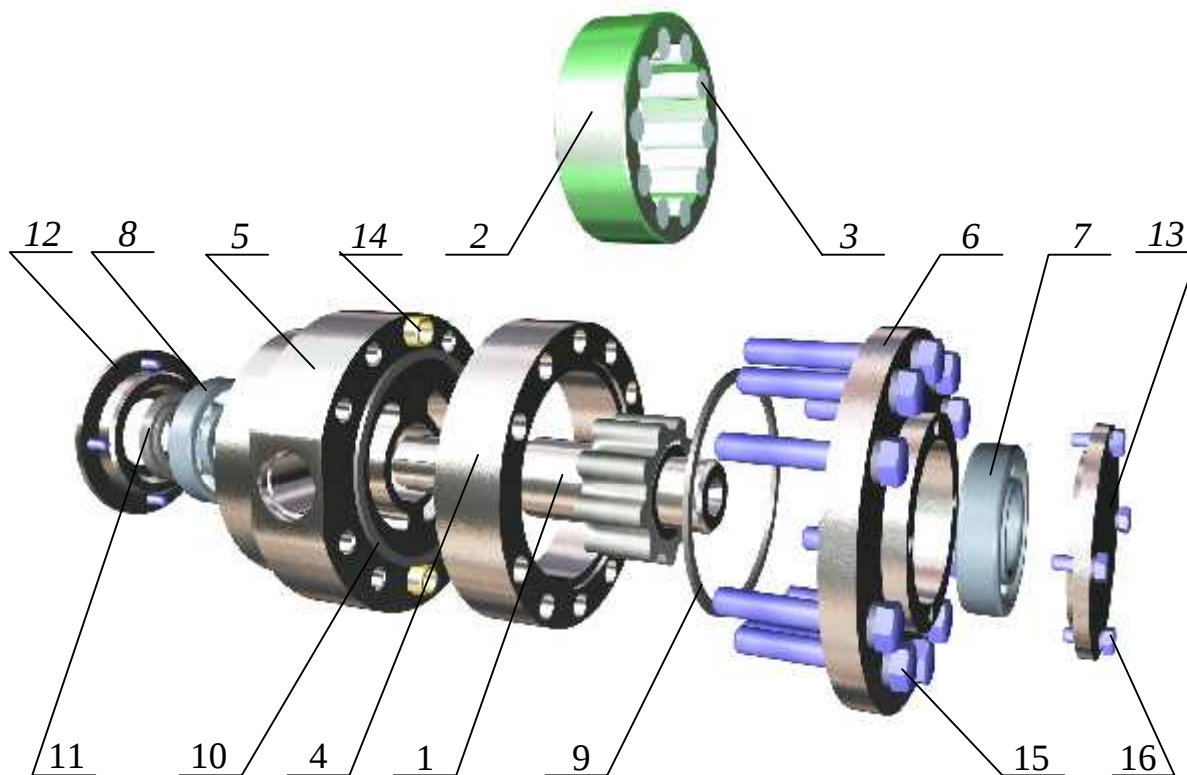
Героторная гидромашина: 1 – вал-шестерня; 2 – ротор; 3 – ролики (зубья); 4 – корпус; 5 – передняя крышка; 6 – задняя крышка; 7, 8 – подшипники качения; 9, 10 – кольцевые уплотнения; 11 – уплотнение вала; 12 – крышка уплотнения; 13 – крышка подшипника; 14 – направляющие; 15, 16 – соединительные болты.
